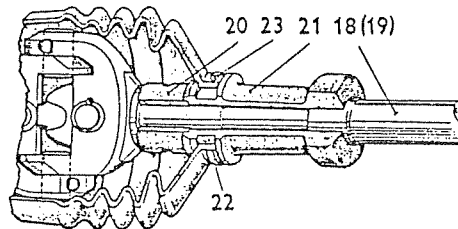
A. Modifierad tätning, inre drivaxel - gummikåpa.
